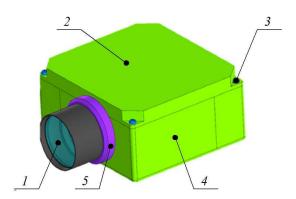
Двухдиапазонное зеркально-линзовое устройство: 1 – объектив; 2 – крышка; 3 – винт; 4 – корпус; 5 – резьбовое кольцо
